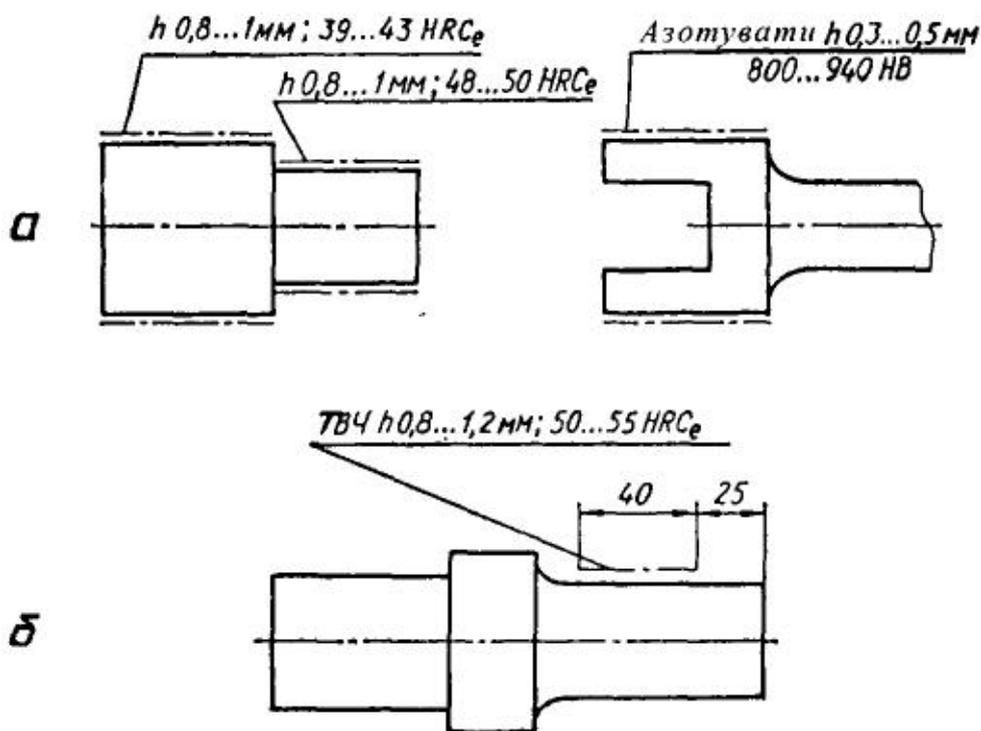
Позначення поверхонь, що підлягають хіміко-термічній обробці.
